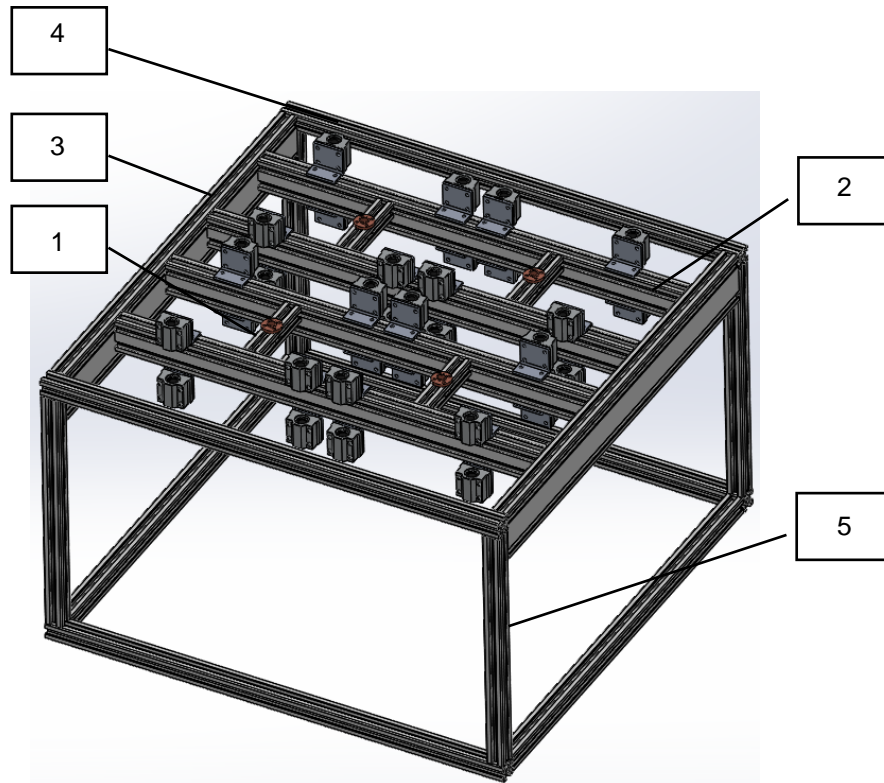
Estrutura de suporte da mesa de impressão.
